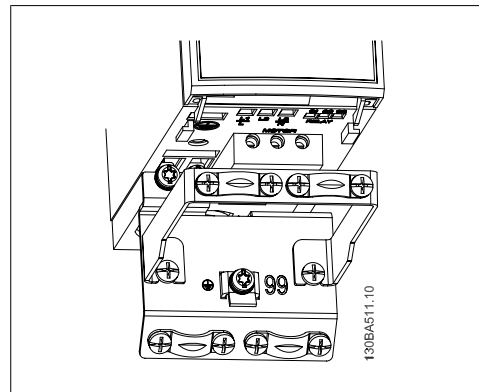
VLT Micro Drive com a placa de desacoplamento
